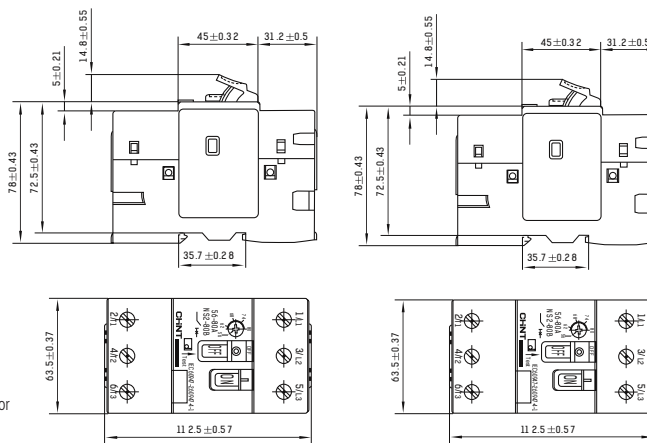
Dimensões gerais e de instalação do Disjuntor Motor
